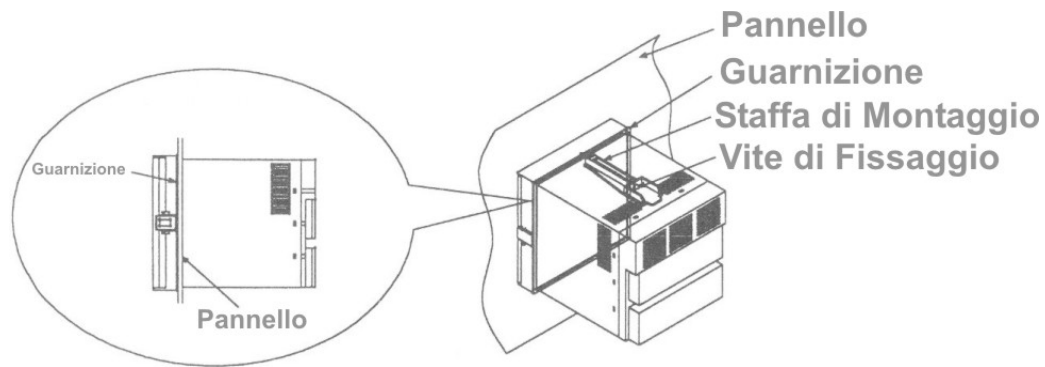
Vista Posteriore del Fissaggio a Pannello
